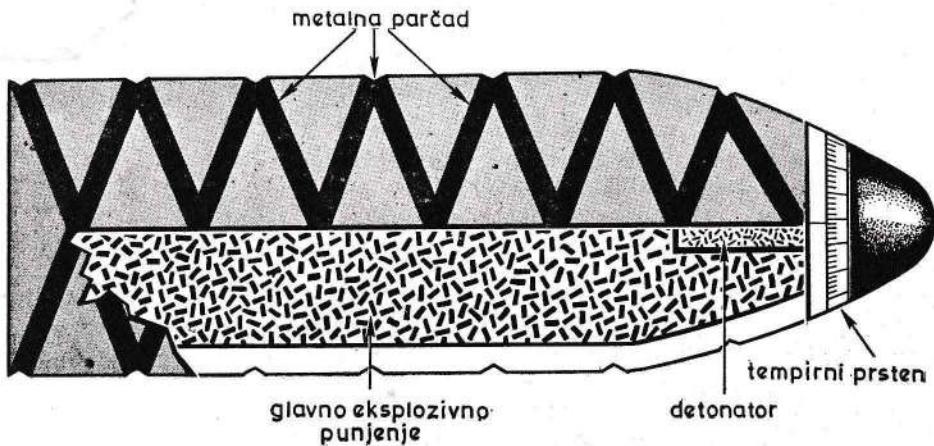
Shema konstrukcije fugasne bojeve glave
